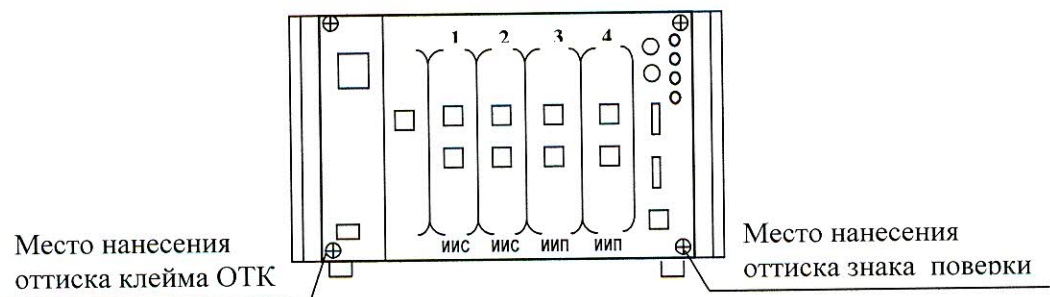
Место нанесения отиска знака поверки (вид прибора сзади)
